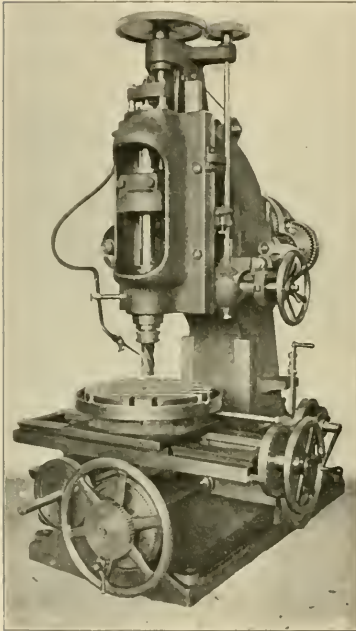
Freistehende, selbstthätige Fräsmaschine.
